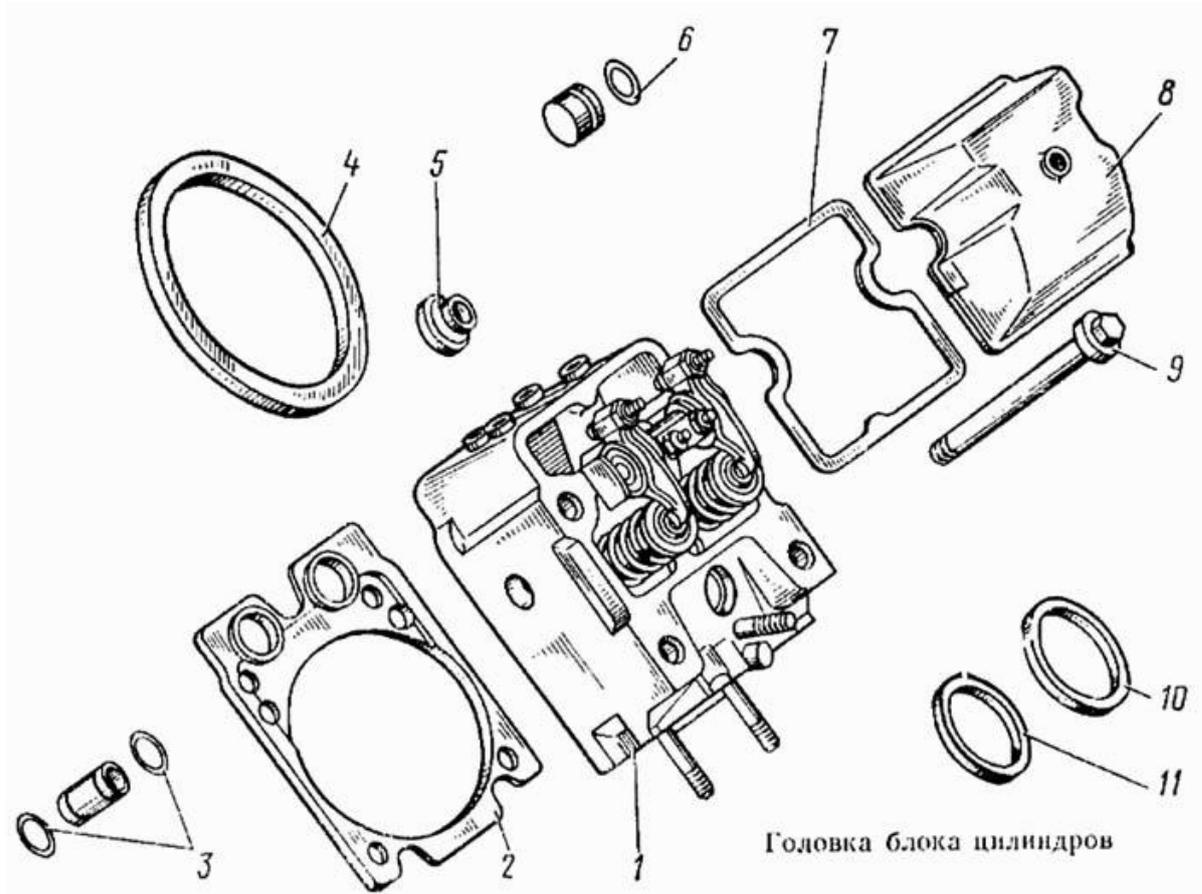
Головка блока цилиндров двигателя КамАЗ-740
